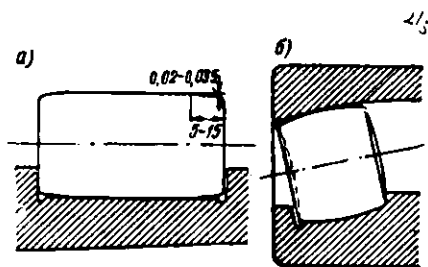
Положение сферического и цилиндрического роликов в подшипнике
